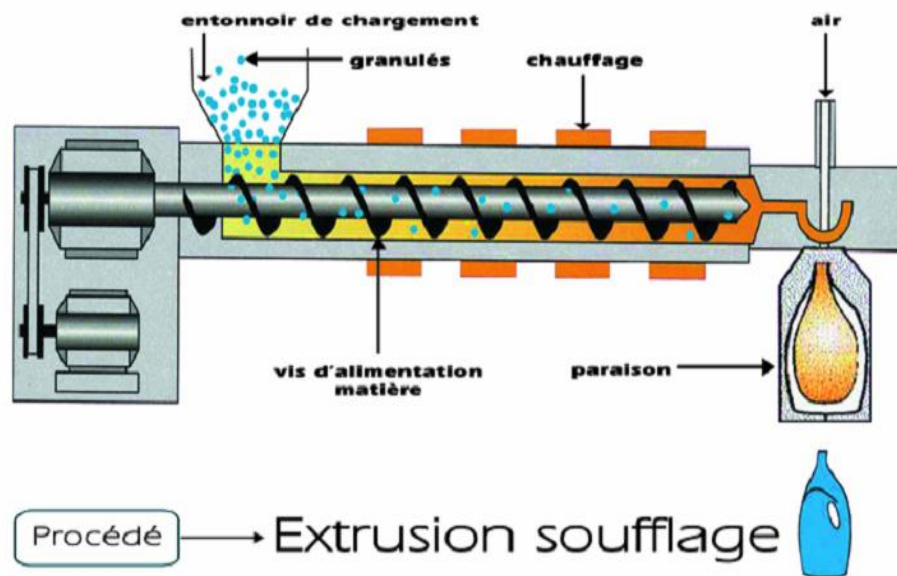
Exemple de procédé d'extrusion-soufflage
